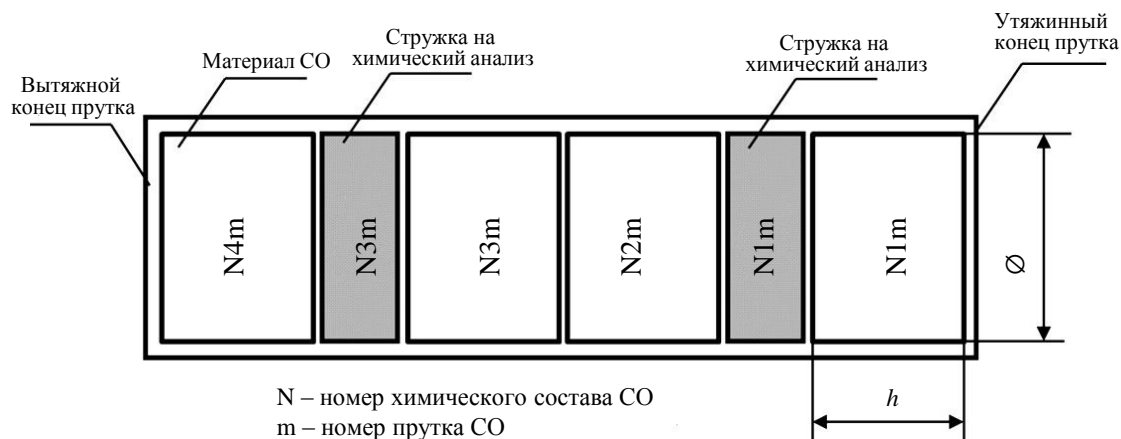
Схема разрезки заготовки стандартного образца (СО)
